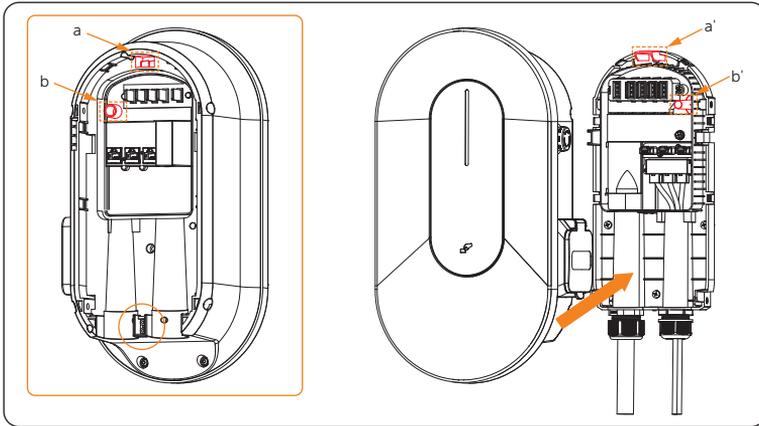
Das Gehäuse auf der Grundplatte ausrichten
